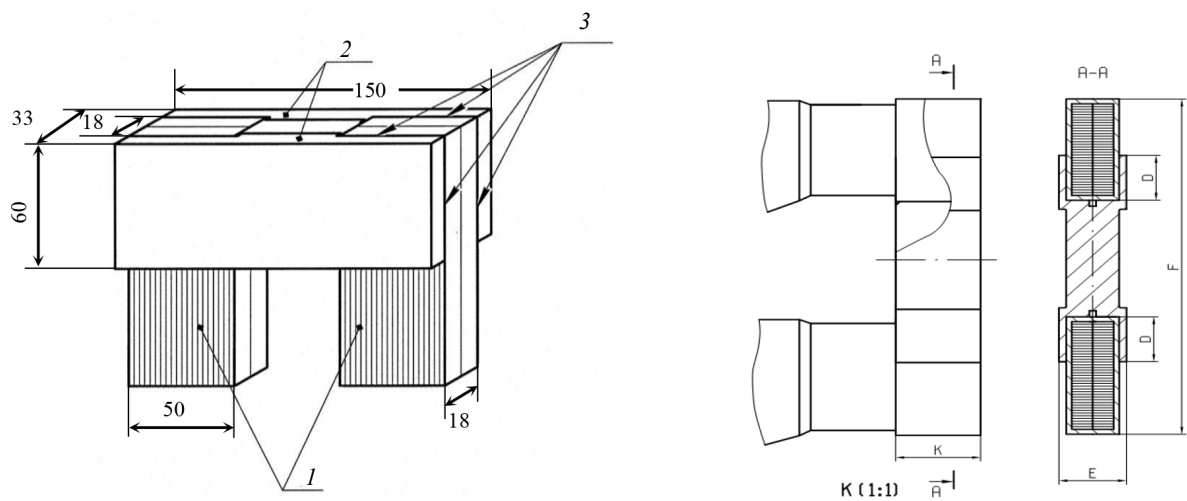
Токоведущие соединения с соединительными планками: 1 — «стержни»; 2 — соединительные планки; 3 — места пайки.
